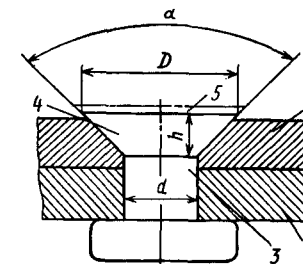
Контроль параметров заклепочного соединения с зачисткой потайных головок заклепок: 1, 2 – соединяемые детали; 3 – заклепка; 4 – головка заклепки; 5 – удаляемая часть головки заклепки
